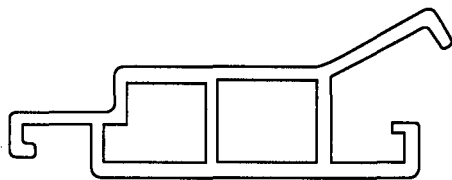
Форма отверстия фильеры для экструзии профиля с близко расположенными стенками [5]
